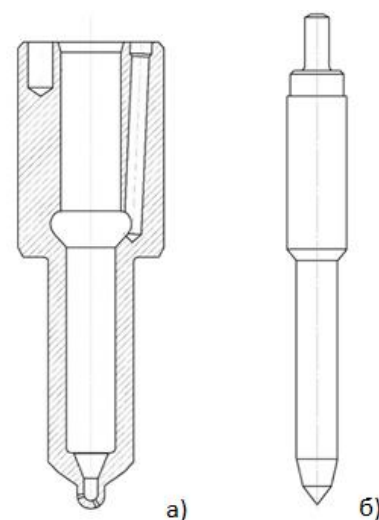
Общий вид распылителя (а) и иглы форсунки (б)
